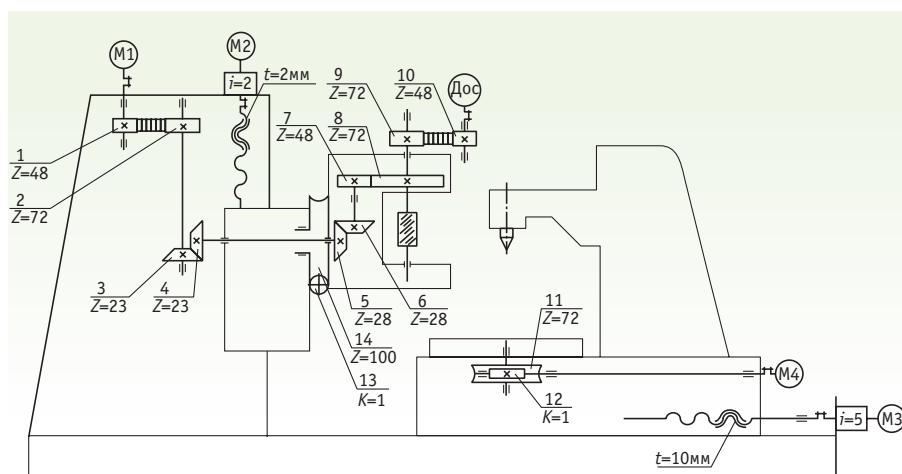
Предлагаемая кинематика модернизированного зубофрезерного станка 53А30
